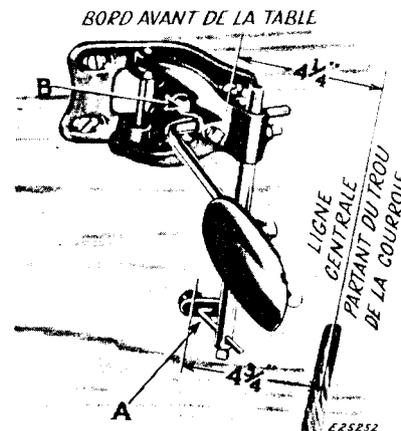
Position de la genouillère sous la table. Machines 410W19 et 410W20
